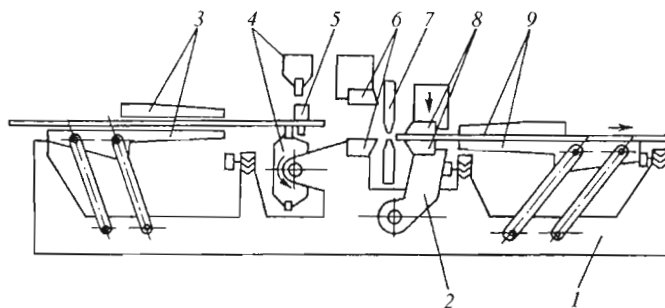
Кинематическая схема комплекса КСО-3201 для стыковой сварки лент:
